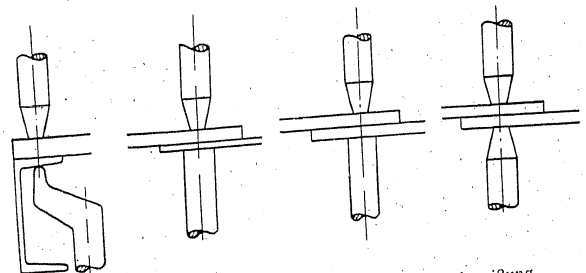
Elektrodenformen für elektrische Punktschweißung
